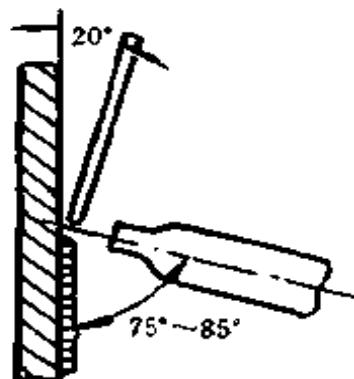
焊枪、焊丝与焊件间夹角
